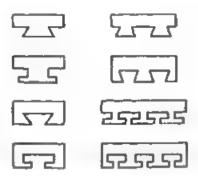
Пластины в различными крепежными выступами для коллекторов на пластмассе
